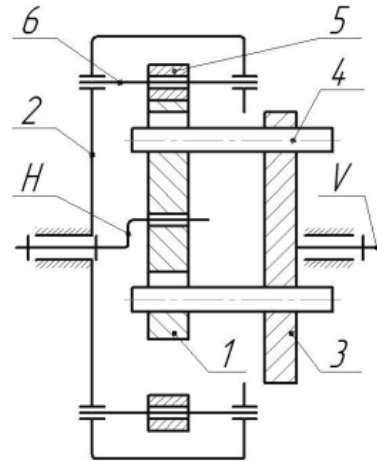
Кінематична схема редуктора типу К-Н-V
